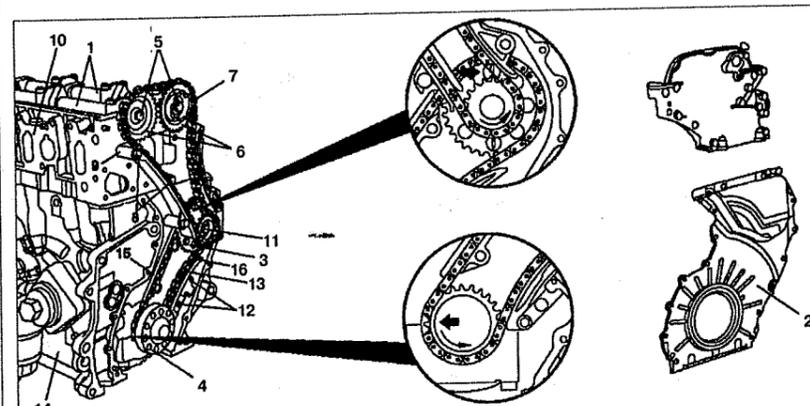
Замена цепи привода: 1. Распределительные валы, 2. Нижняя крышка ГРМ, 3. Шкив промежуточного вала, 4. Зубчатый шкив коленчатого вала, 5, 8, 11, 12. Болт, 6. Шкивы распределительных валов, 7. Верхняя цепь, 9, 15. Направляющий рычаг, 10. Головка блока цилиндров, 13. Натяжной рычаг, 14. Блок цилиндров, 16. Нижняя цепь.
